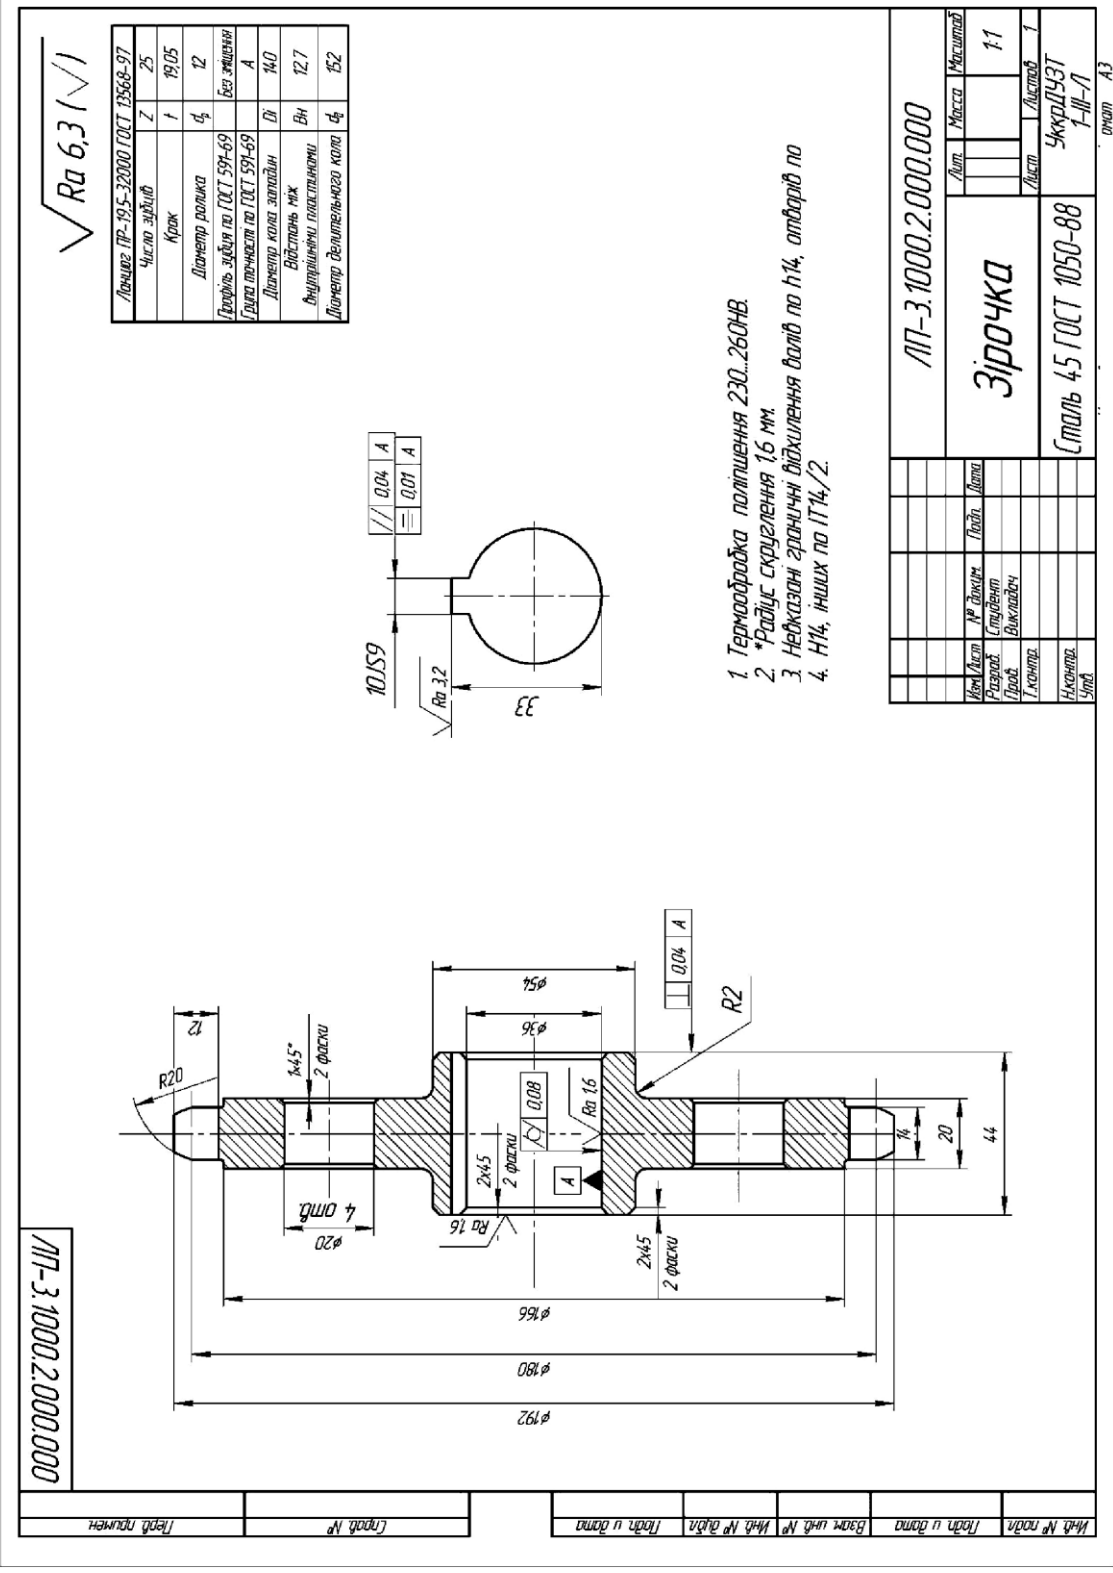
Робоче креслення зірочки ланцюгової передачі
